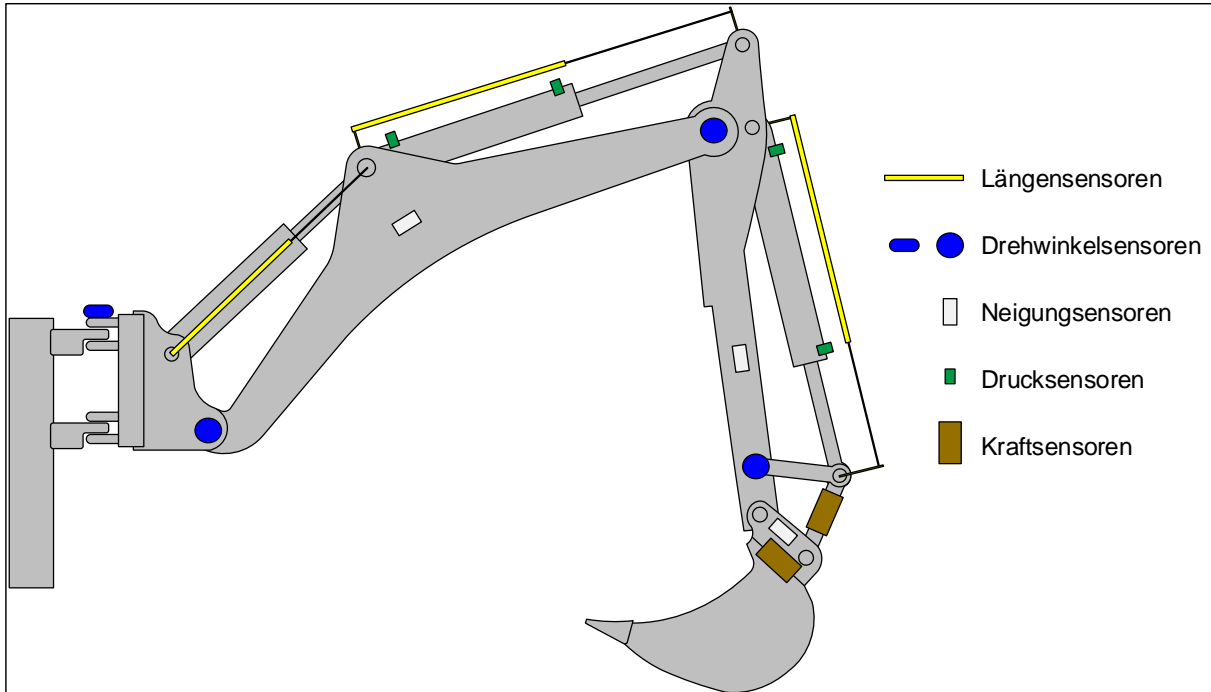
Integration einer Zug-/ Druckkraftmessung in die Koppel
